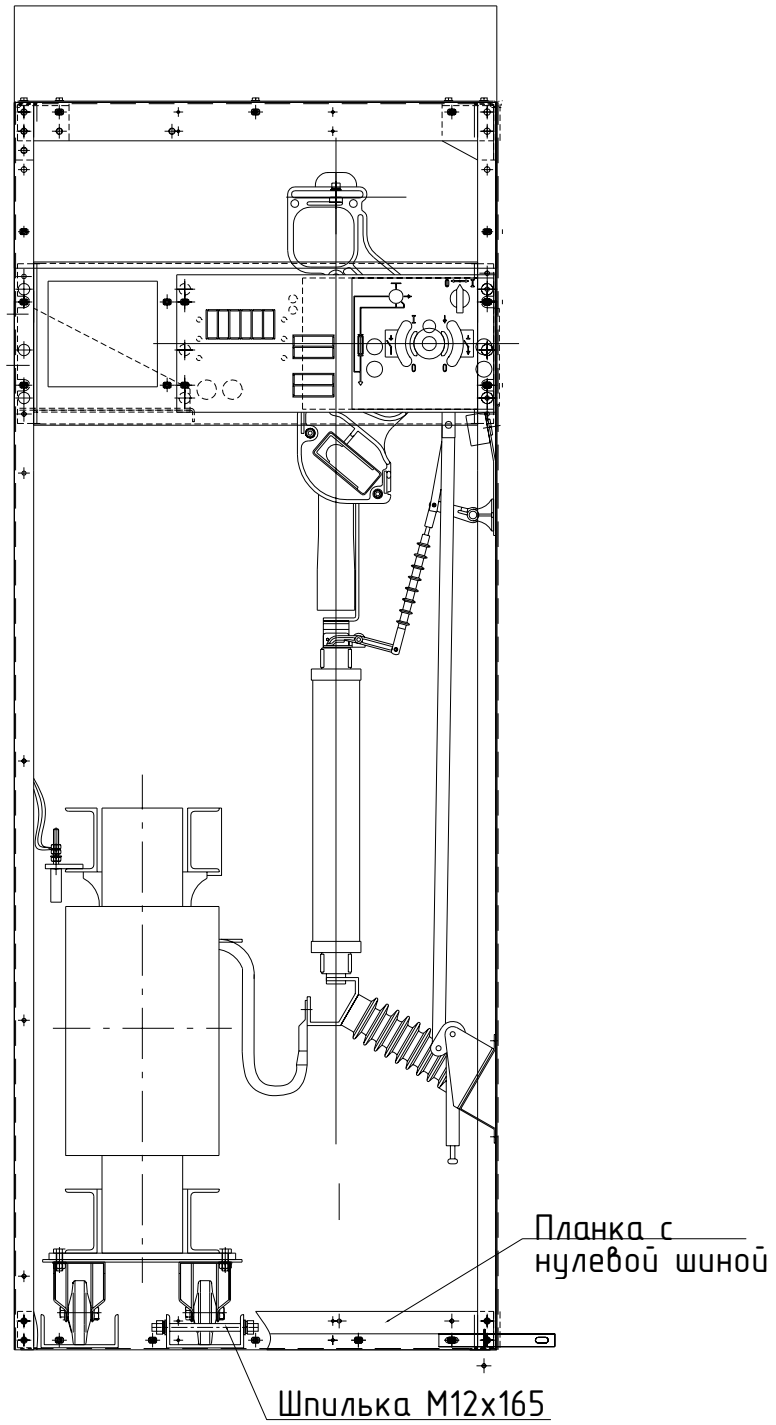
Монтаж ячеек схемы 22 габарита1.
